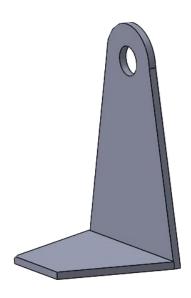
Pieza de agarre Fuente: Elaboración Propia
